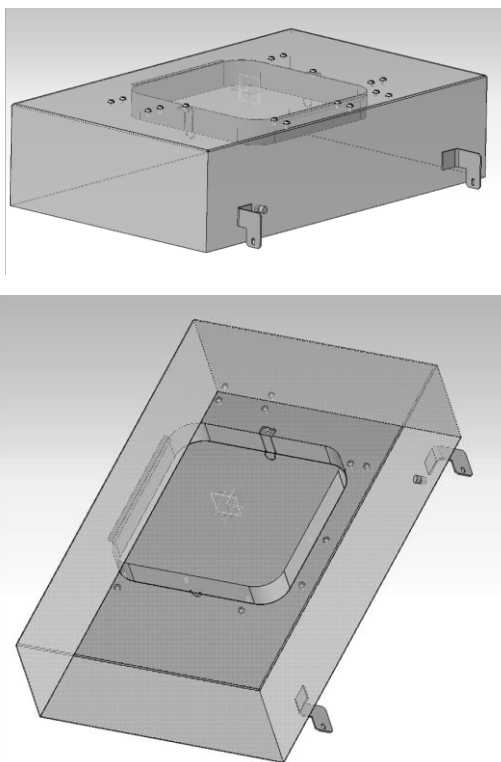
Крышка мойки – вид снаружи и снизу
